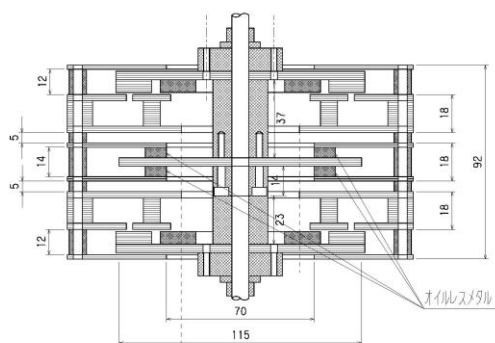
平面転がりベアリング支持方式 図 2-2-15 鋼球式平面ベアリング支持方式
